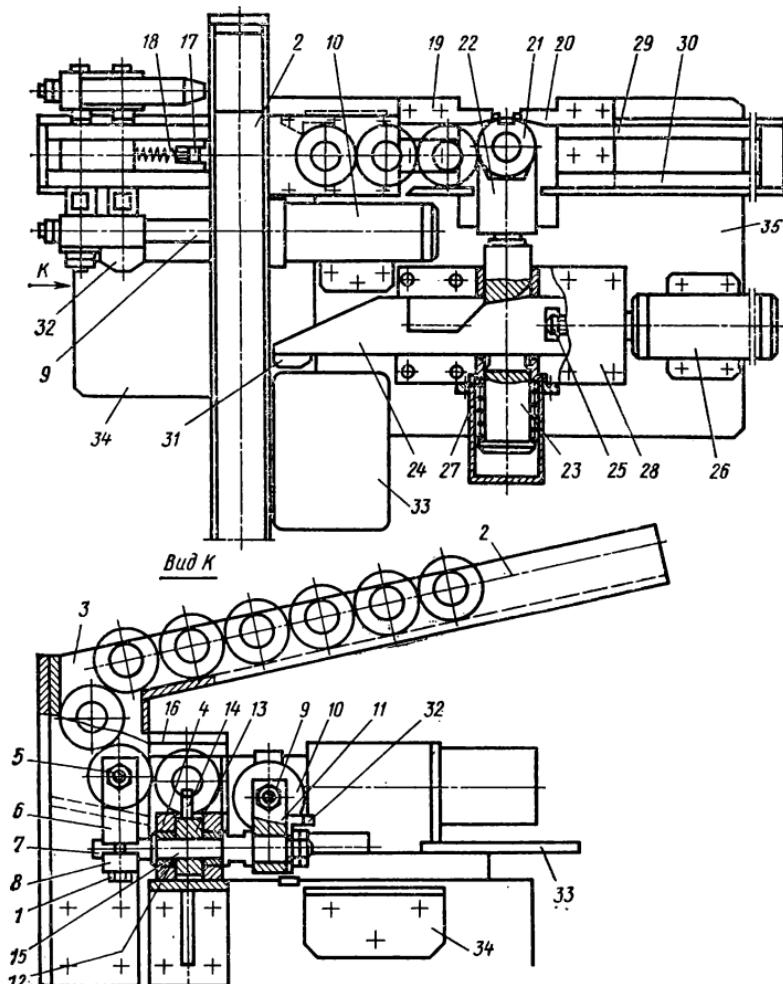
Загрузочно-разгрузочное и зажимное приспособление для протягивания паза в заготовке гайки рулевого управления
